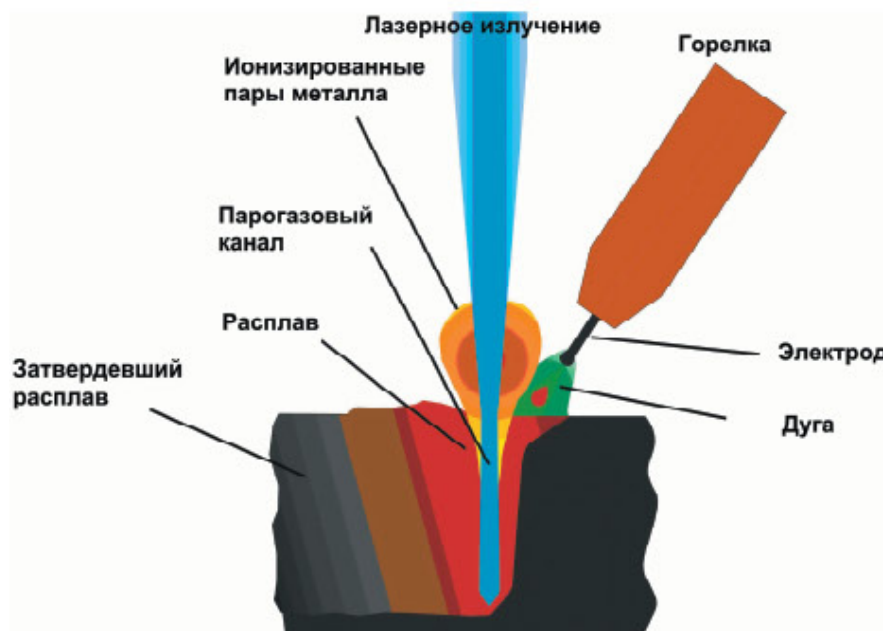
Схема процесса лазерно-дуговой сварки
